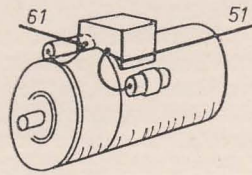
Entstörung einer Lichtmaschine mit eingebautem Regler
